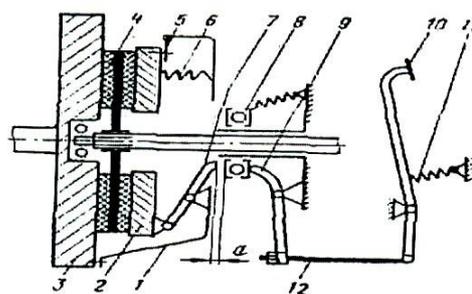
Кінематична схема однодискового зчеплення з периферійними пружинами та механічним приводом керування
